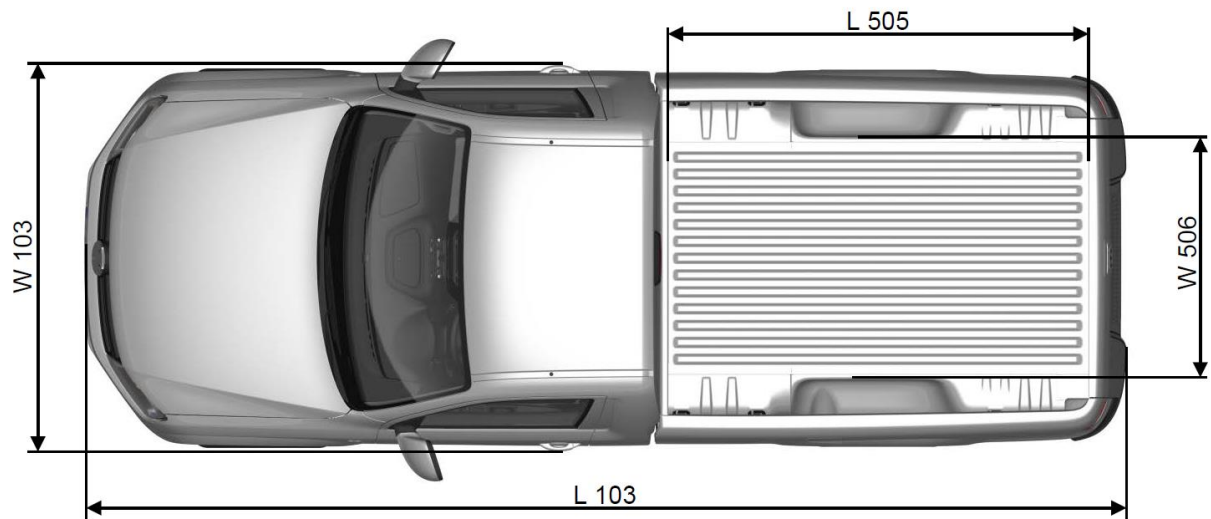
Draufsicht Amarok-SC (Single Cab)
